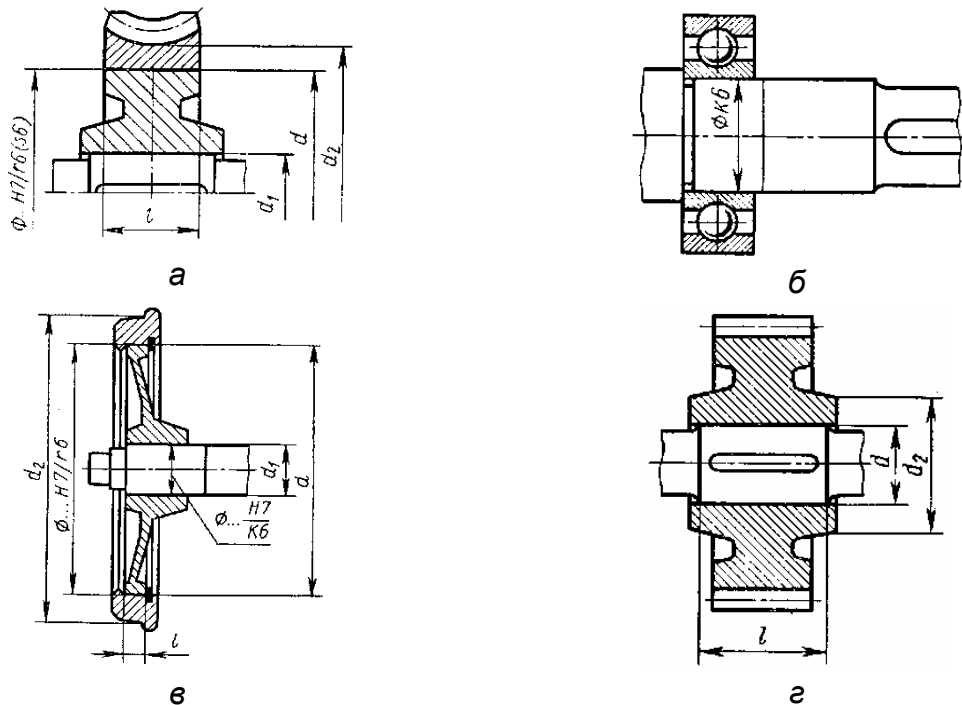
Соединения с натягом: а – в составном червячном колесе; б – при посадке подшипников на вал; в – в локомотивных колесах; г – в соединении зубчатых колес с валами
